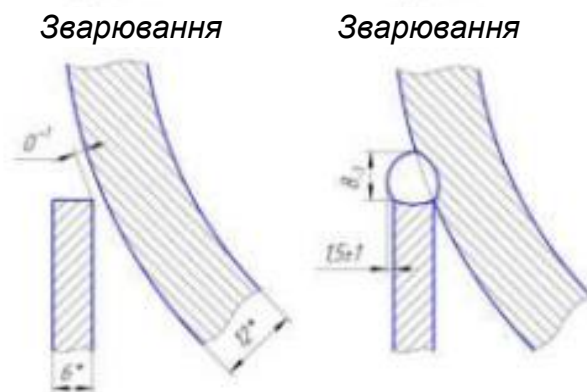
Зварний шов № 2 приварювання нижнього днища до обичайки опорної
